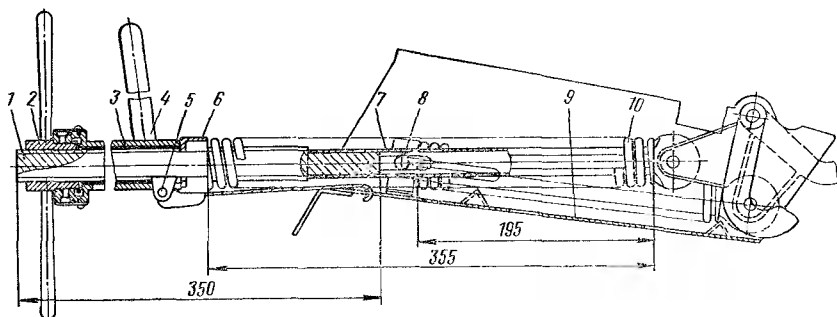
Приспособление для постановки и снятия пружины петли багажника
